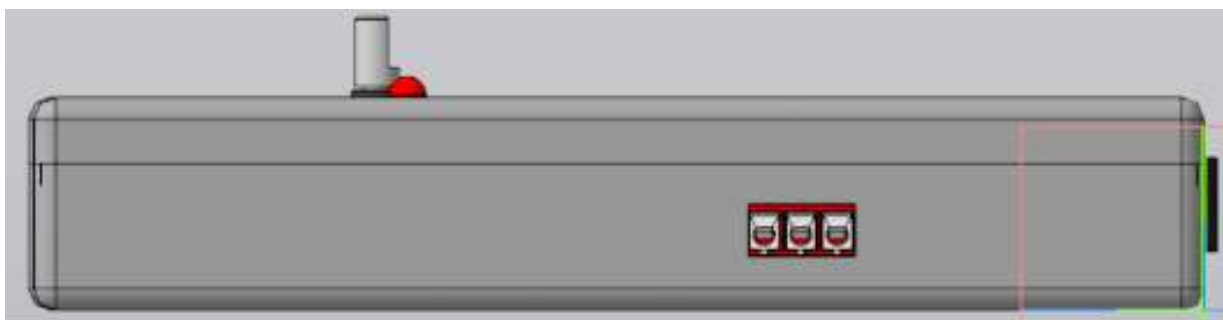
3D модель пристрою в корпусі, вид збоку
